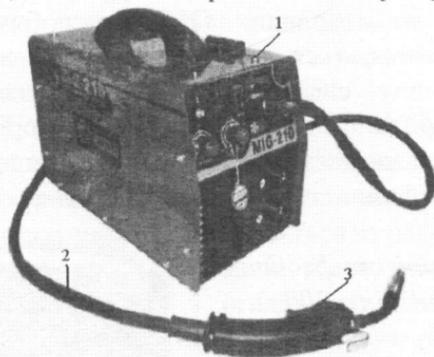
Зовнішній вигляд одного з напіваавтоматів інверторного типу для зварювання за способом MIG: 1 – корпус напіваавтомата, який вміщує джерело струму для зварювання – інвертор, систему управління, яка управляє потужністю дуги тощо; 2 - . зварювальний кабель для підключення затиску до зварюваної деталі з рукавом для подачі газу і зварювального дроту; 3 – пальник
